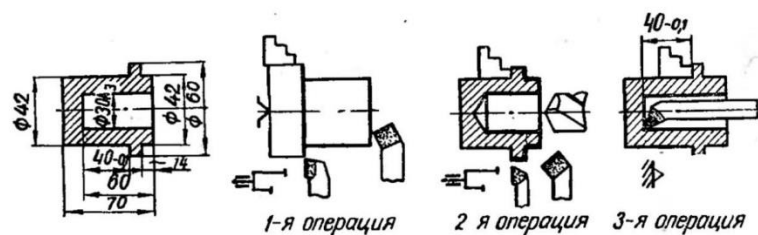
Обработка стакана из одной или штучной заготовки при высокой точности расположения дна относительно фланца.
